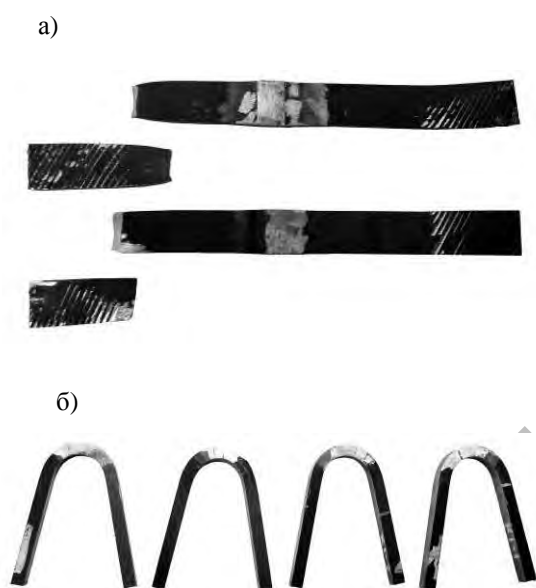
Внешний вид сварных образцов после механических испытаний: а – статическое растяжение; б – статический изгиб (SBB) 180°
